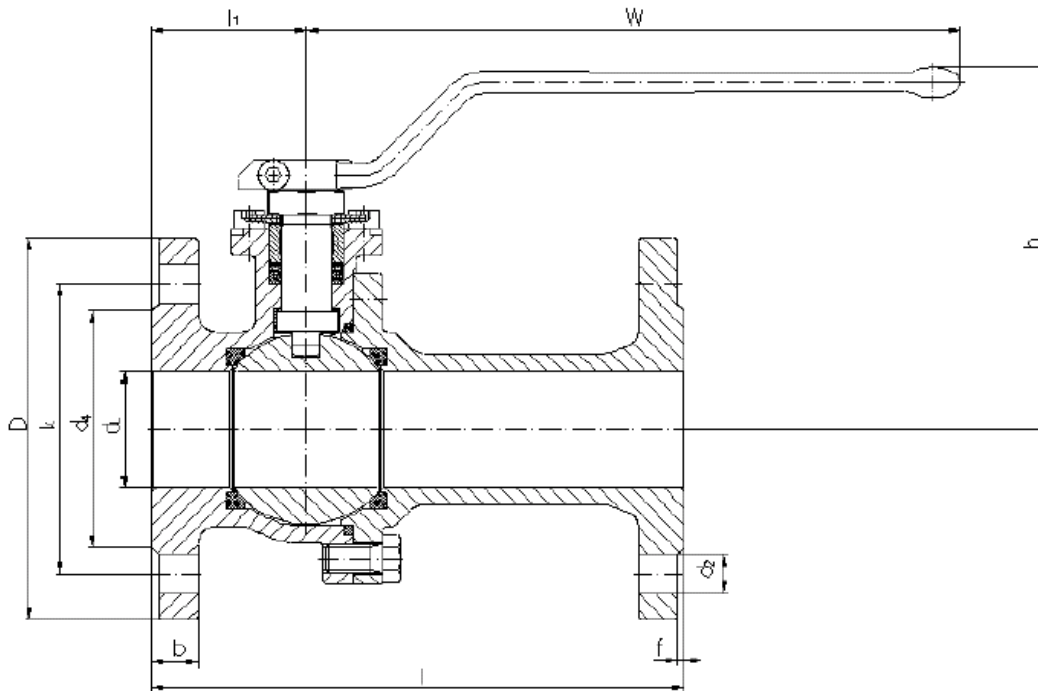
Kugelhahn mit Flanschanschluss nach DIN EN 1092-1 Form B1; Baulänge Grundreihe 28 (lang) nach EN 558-1 (F17 nach DIN 3202 Teil 1)
